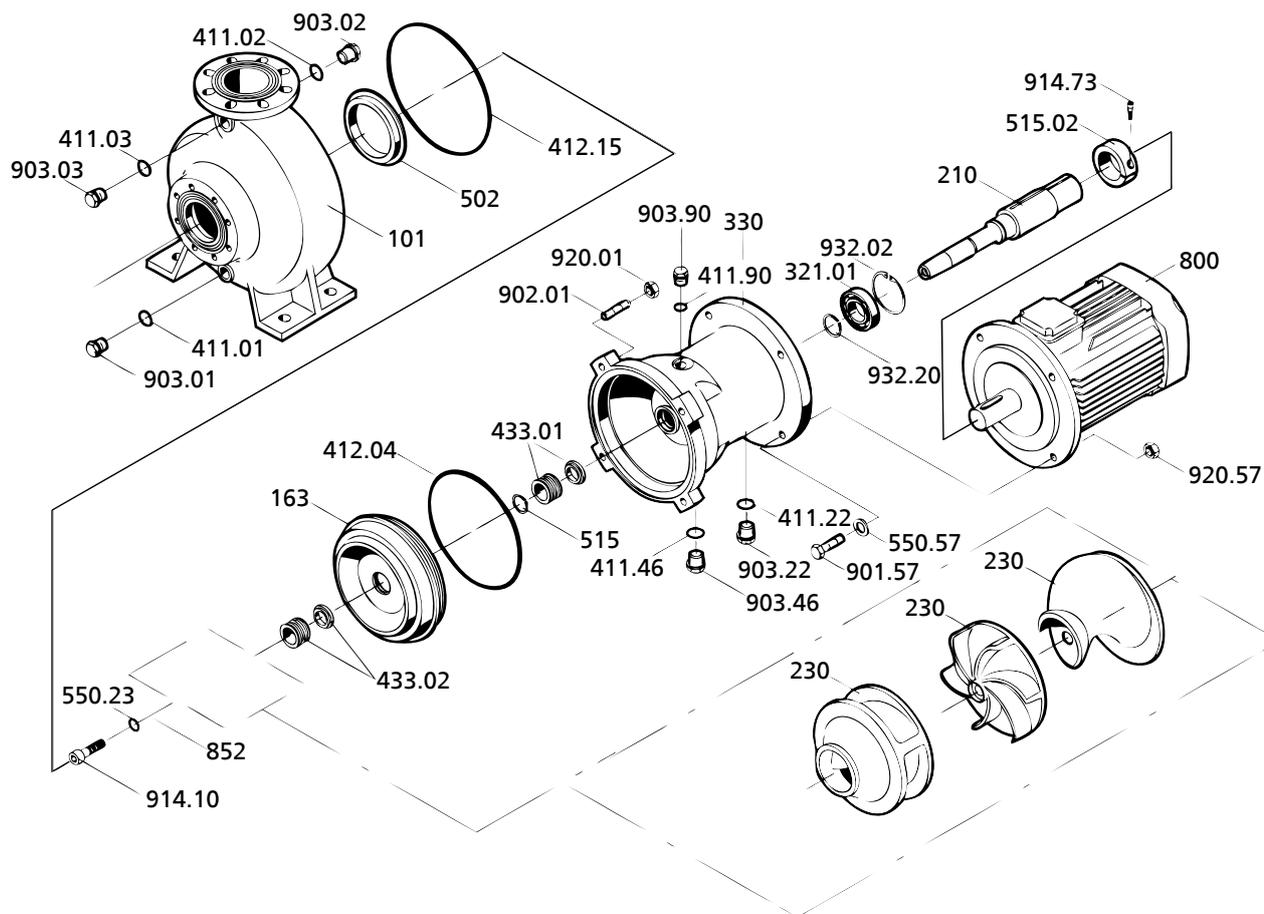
Покомпонентный сборочный чертеж Sewabloc
